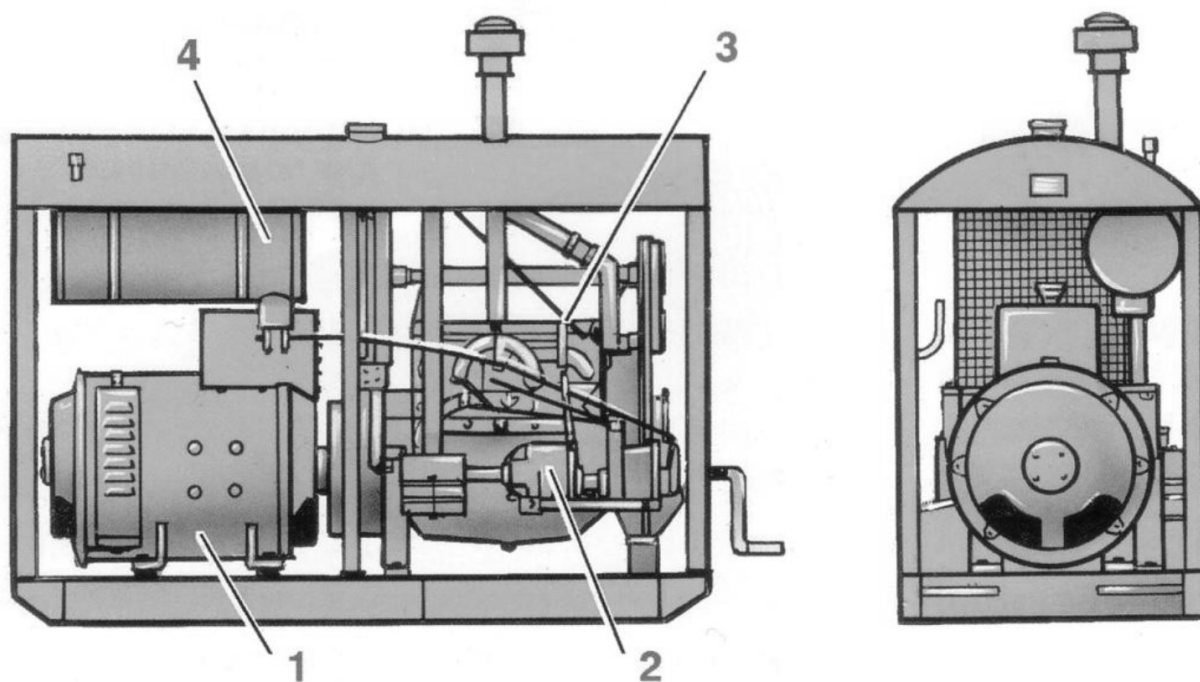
Внешний вид сварочного агрегата:
